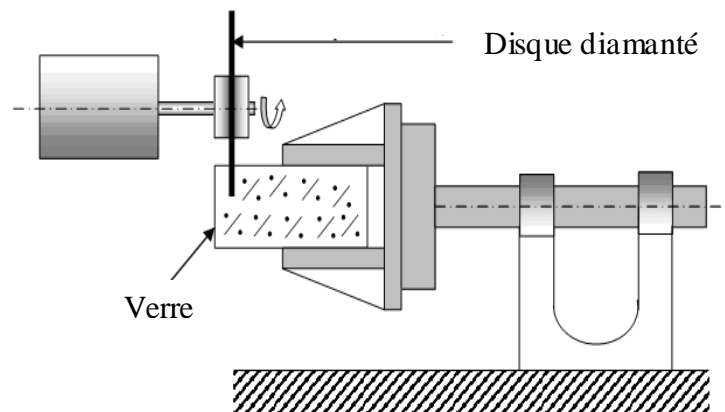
Principe de découpage du verre par disque diamanté [Bel08].
